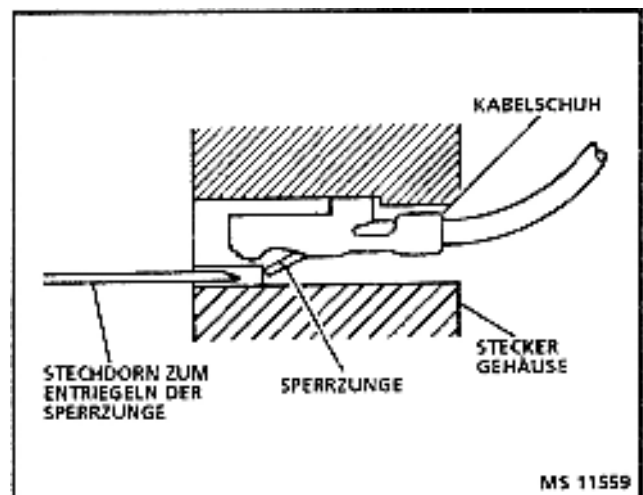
Typische Pull-to-Seat Steckverbindung und Kabelschuh
